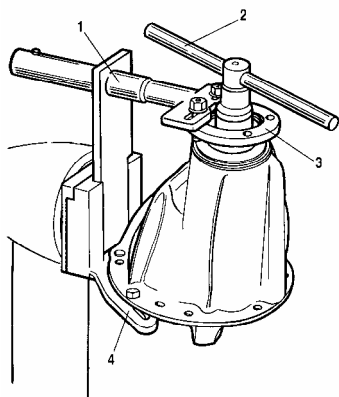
Отвертывание гайки ведущей шестерни:
